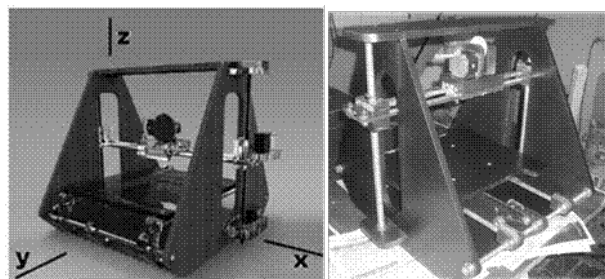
A la izquierda el diseño CAD del sistema y a la derecha la impresora construida
